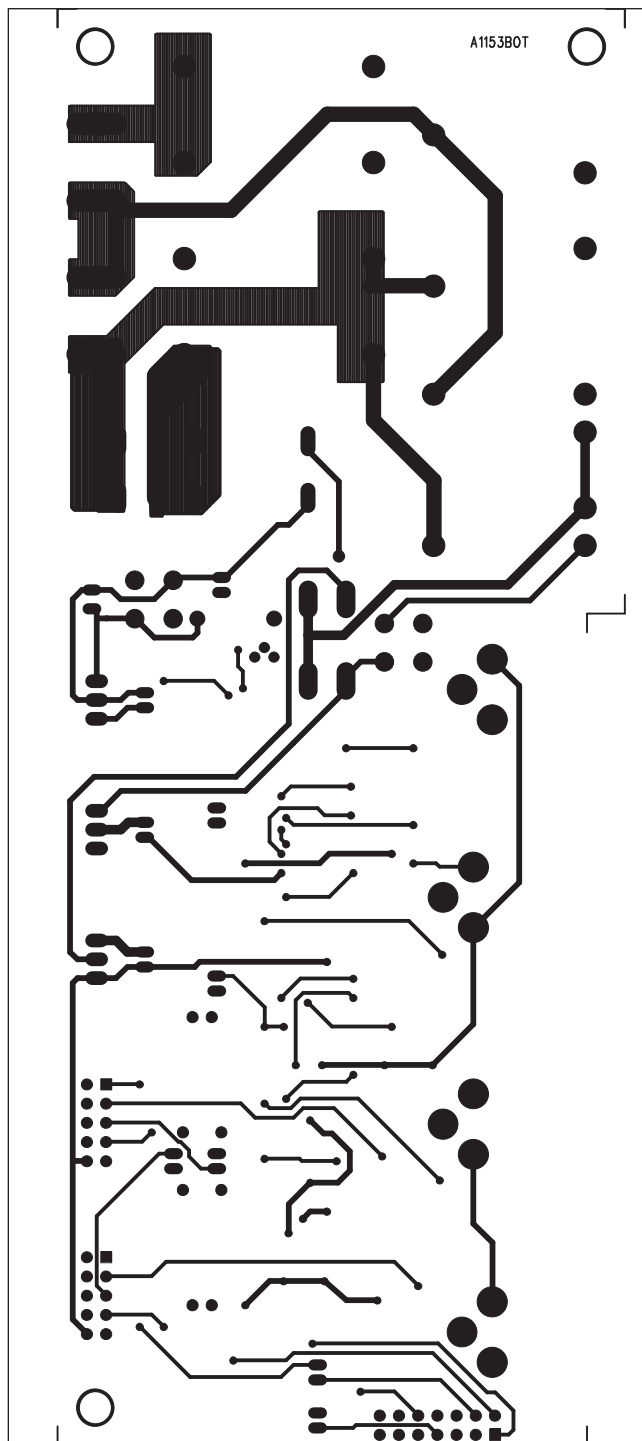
Obrazec desky spojů pomocné desky (strana TOP)
